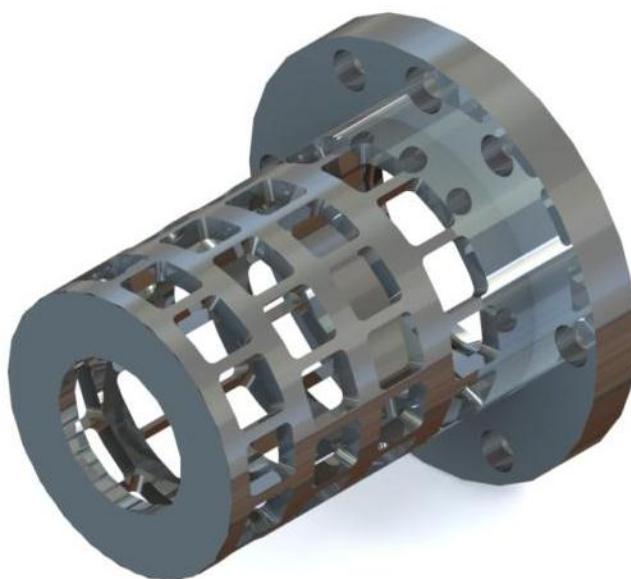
Твердотельная модель детали «Сепаратор»
